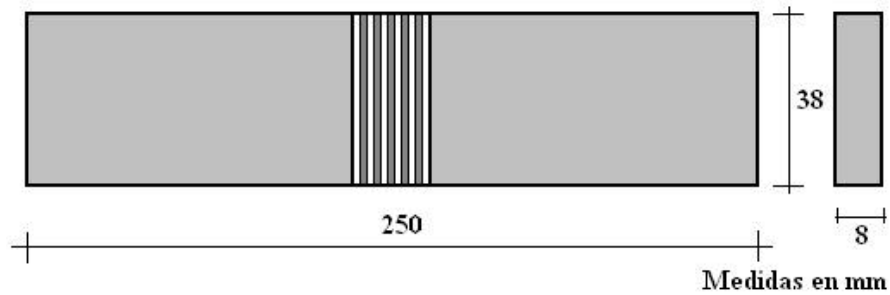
Diseño de probeta para ensayo de Dobleza (cara y / o raíz) de la junta soldada de acuerdo a la regla QW-462.3(a) del Código ASME sección IX.
